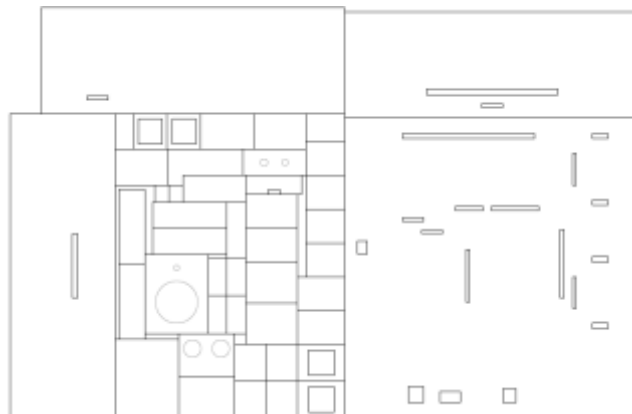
Plantilla vectorial para el corte laser de la plancha de acrílico.
